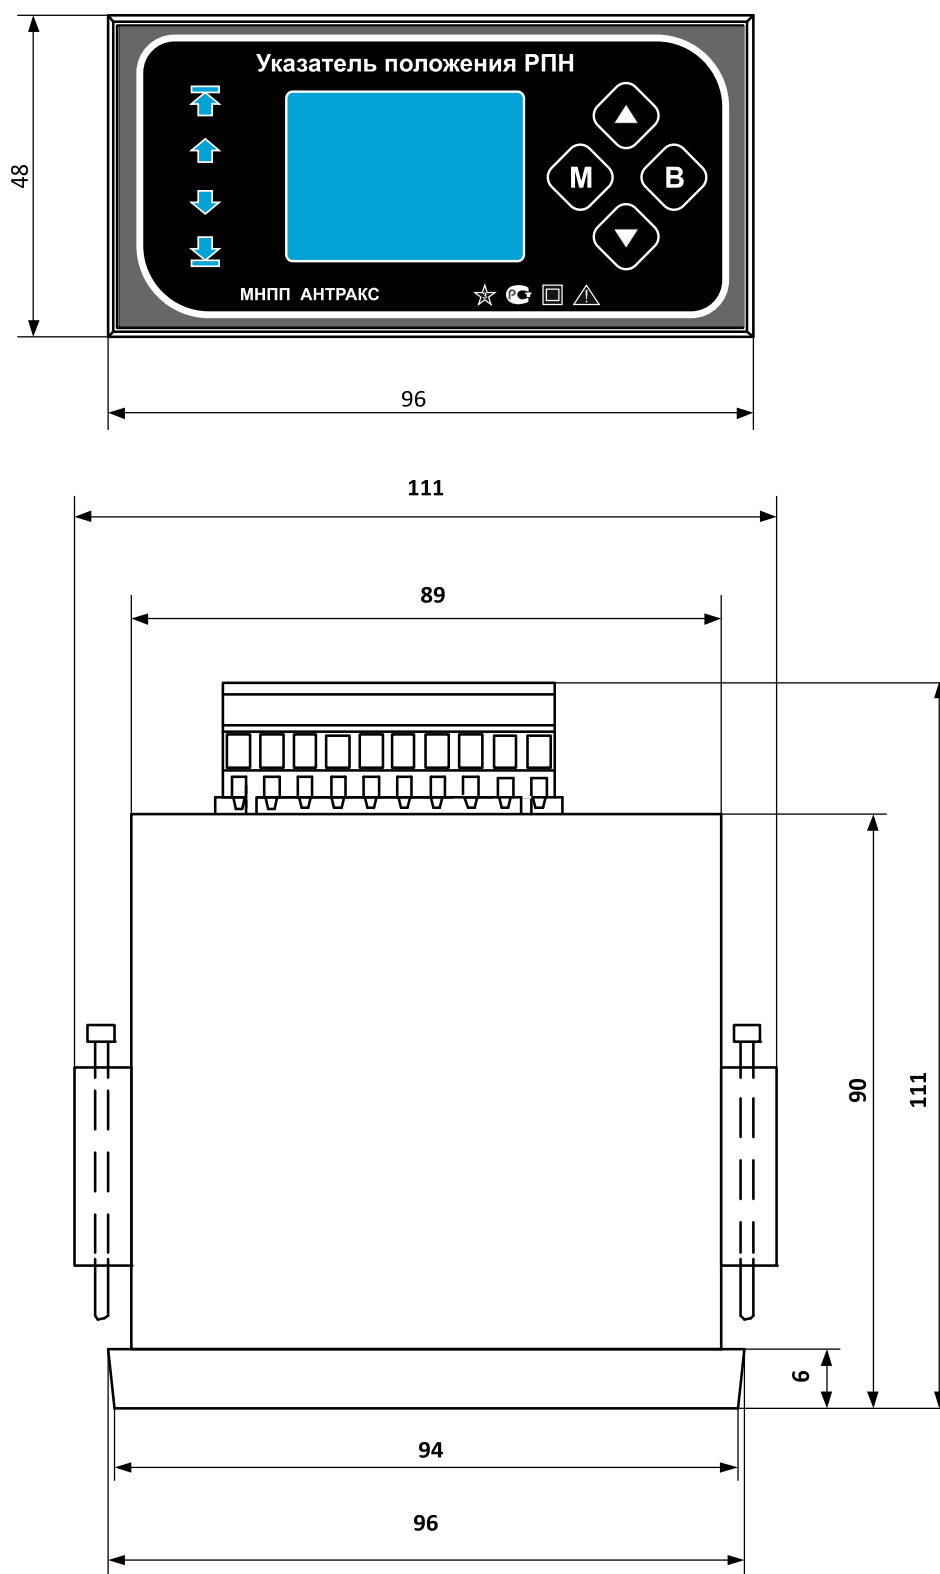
Габаритные размеры щитового варианта указателя положения РПН УП 4-Е
